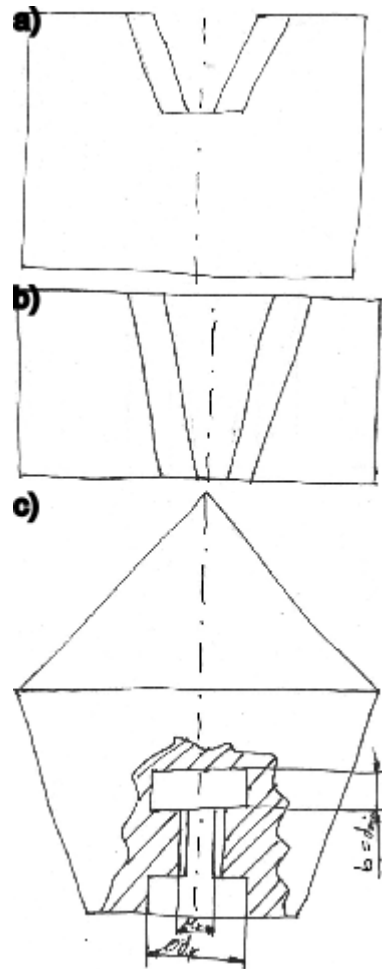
a) Kopfaufnahme Keilausführung, Ansicht oben; b) Kopfaufnahme Keilausführung, Ansicht vorn; c) Detailansicht Wellenkopf Keilausführung
